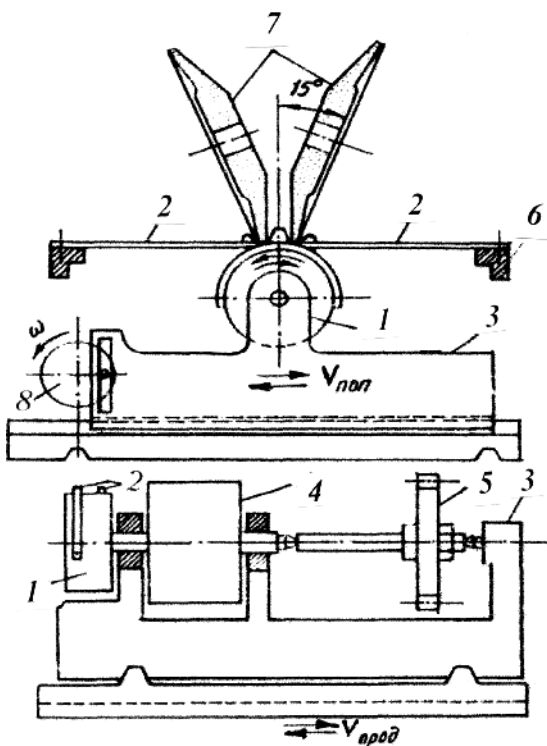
Схема работы зубошлифовального станка 5851 МААГ.
